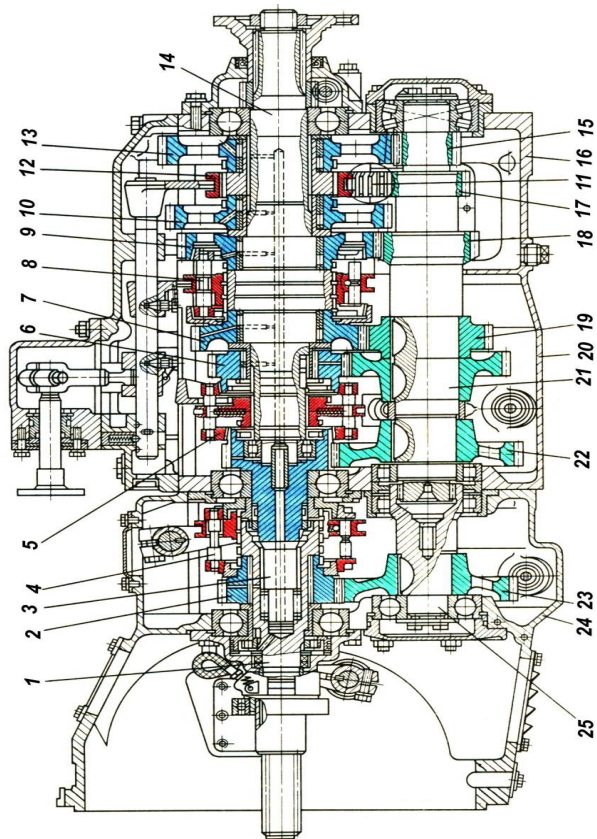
Устройство коробки передач автомобиля КамАЗ-5320:
